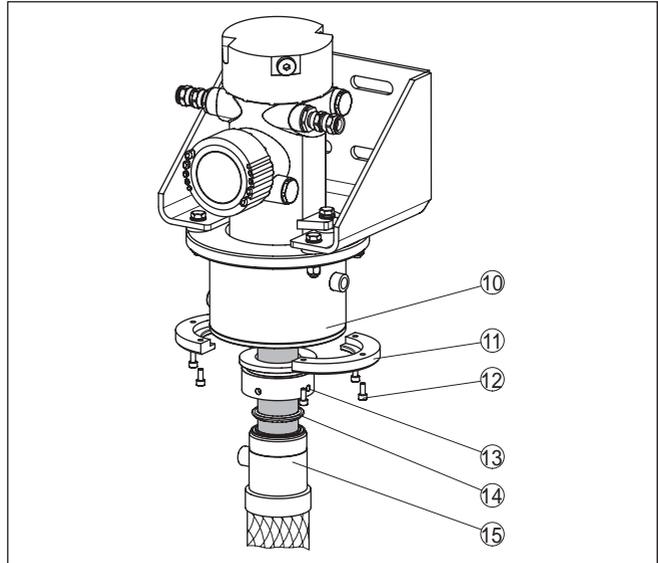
Montaje de la refrigeración de escintilador - parte superior
